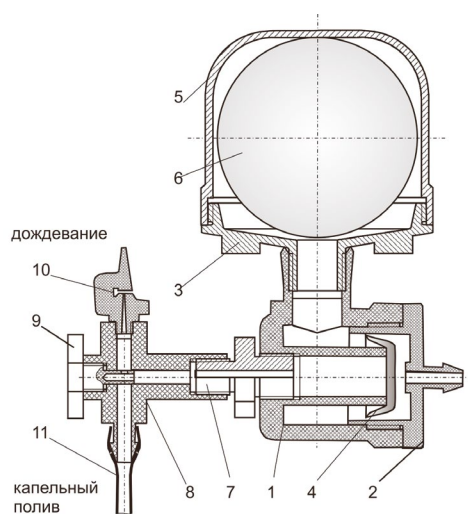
Импульсный капельно-дождевальный водовыпуск: 1 – корпус; 2, 3 – крышка; 4 – полупроводниковая манжета; 5 – колпак; 6 – эластичный шар; 7 – переходник; 8 – корпус крана; 9 – переключатель; 10 – дождевальная насадка; 11 – поливная трубка
